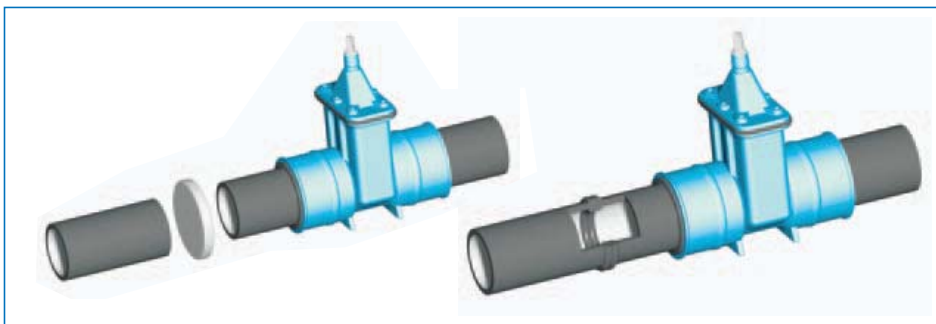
Prinzip des Heizelementstumpfschweißens
